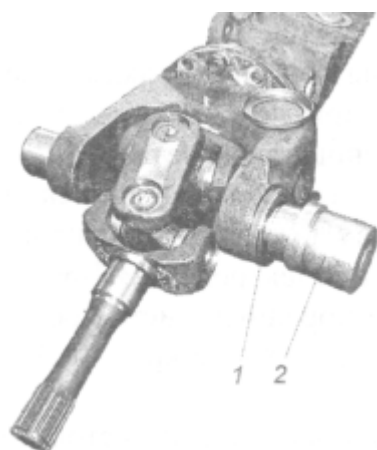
Запрессовка уплотнения «Stefa»:
